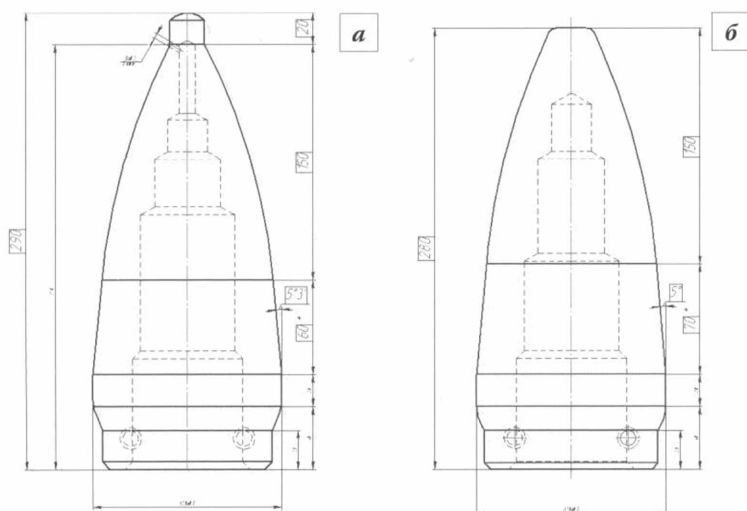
Изменение конструкции прошивной оправки диам. 120 мм: а – стандартная и б – опытная калибровки
